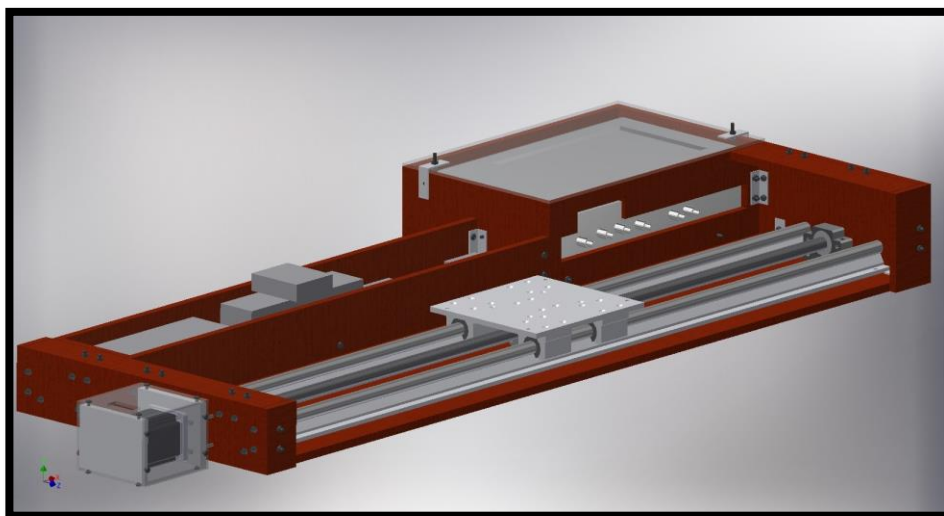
Mecanismo de posición lineal (Fuente: el autor)
